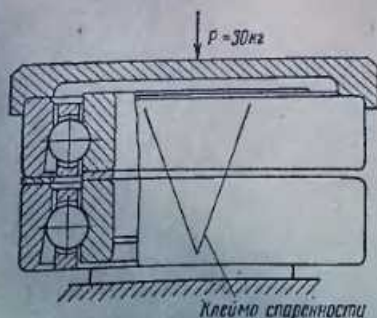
Схема приложения нагрузки на подшипники переднего хода фланца вала
